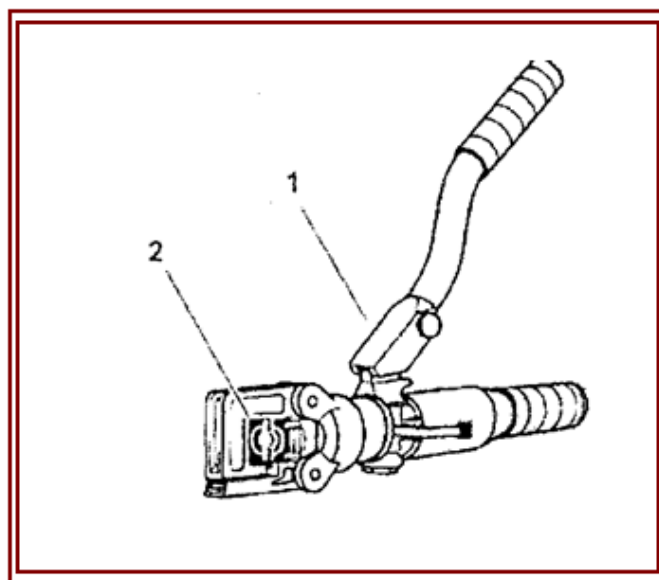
Ручной пресс для запрессовки соединительных втулок.
